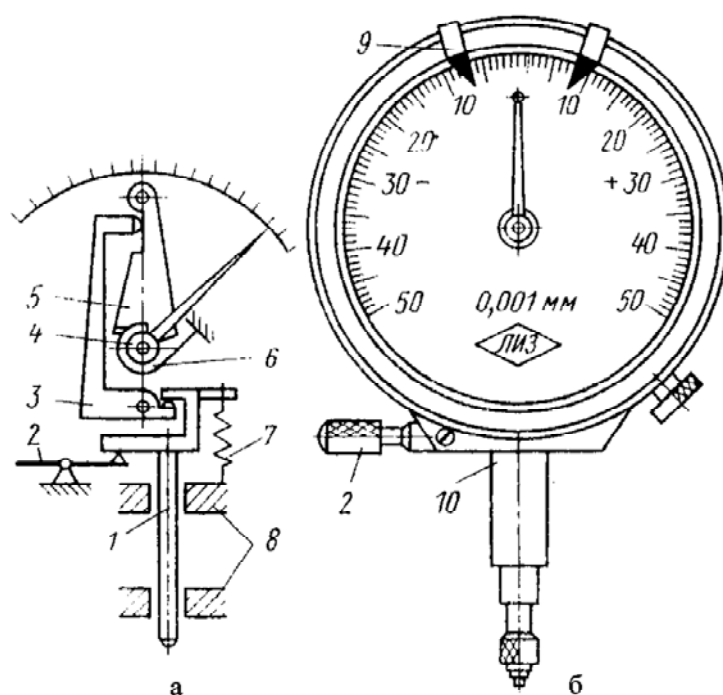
Рычажно-зубчатая измерительная головка ИИГ: а – схема; б – общий вид
